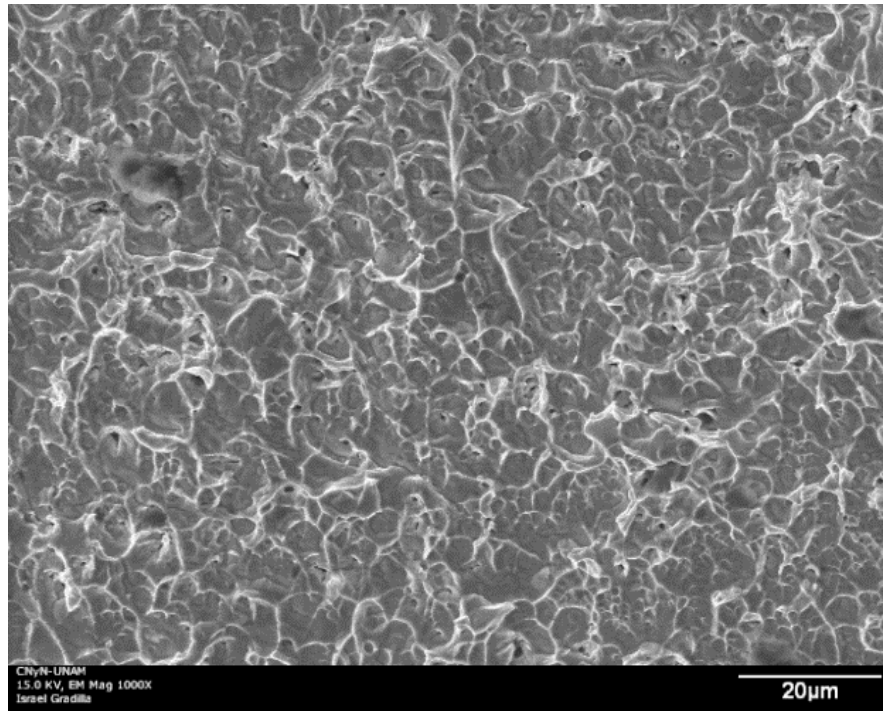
Vista bajo MEB de K3XF-C a 1000x. Se puede apreciar una fractura transgranular, típica de una fractura dúctil.
